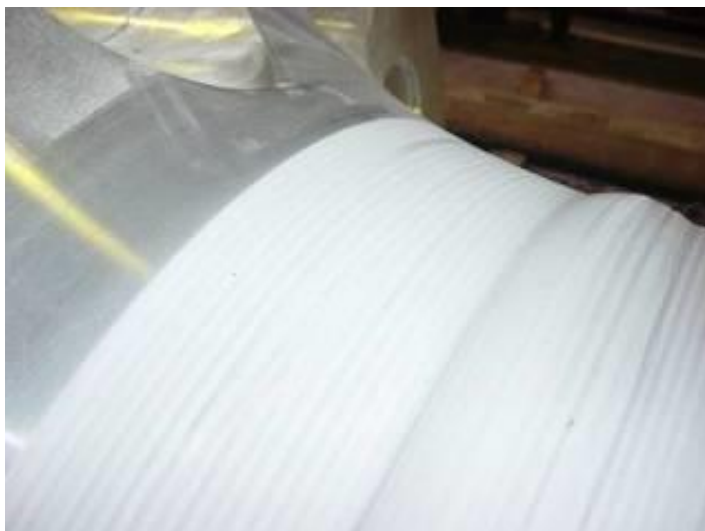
Внешний вид защитного покрытия на наружной стороне секции по сварному шву
